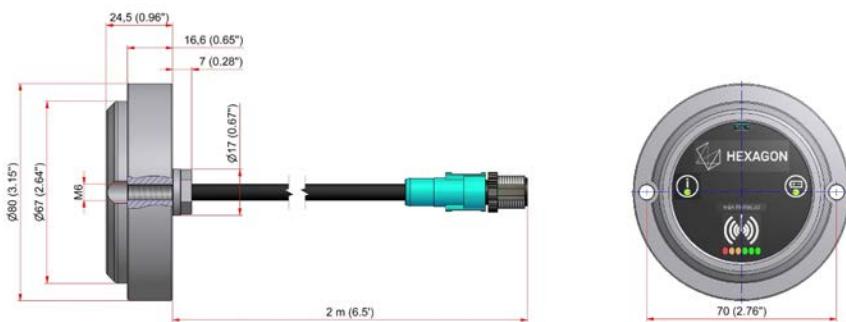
Dimensioni RWR95.50-A-PLUG-8 (uscita del cavo assiale)
